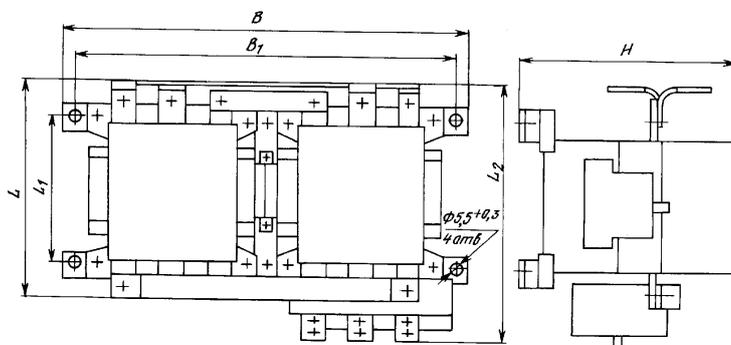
Габаритные, установочные размеры пускателей реверсивных типов ПМ12-080, ПМ12-100, ПМ12-160
